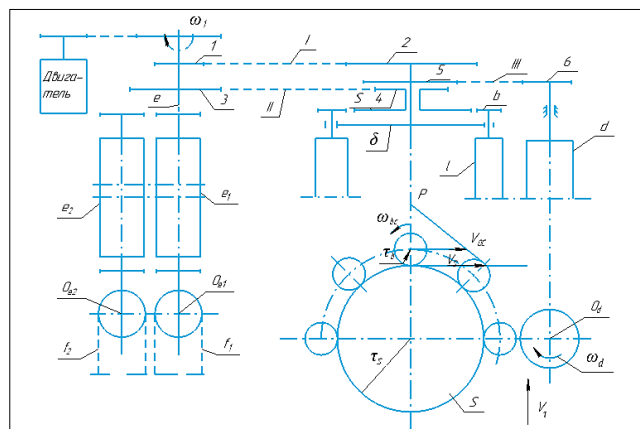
Схема вертикального початкоотделяющего аппарата: 1-6 – колеса передаточного механизма; δ – планетарный барабан; b – вальцы; S – солнечное колесо; τ_δ, τ_s, τ_c – радиусы барабана; ω_δ, ω_s, ω_c – угловые скорости барабана; I, II, III – сателлиты и цепочные контуры; e₁, e₂ – стеблепротягивающие вальцы; f₁, f₂ – стеблеподающие цепи; O_s, O_δ, O_c – центры солнечной шестерни, барабана и сателлита; d – гладкий барабан
